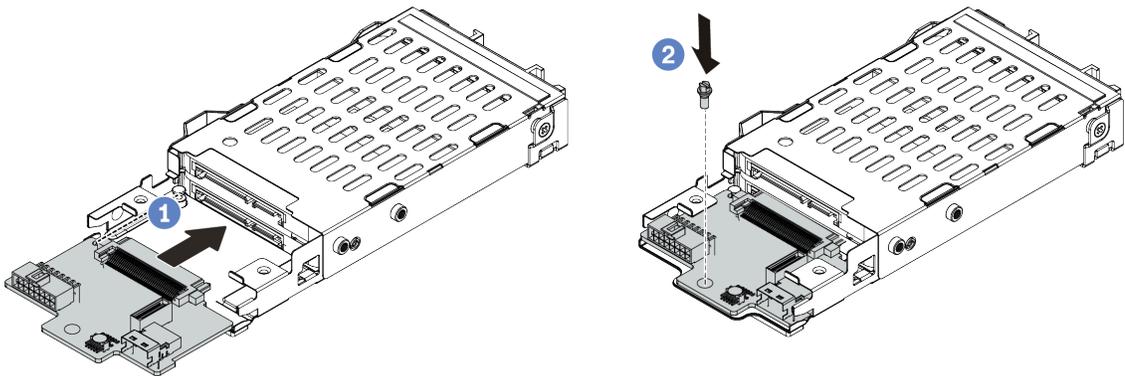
Installazione del backplane dell'unità da 7 mm (parte inferiore)
